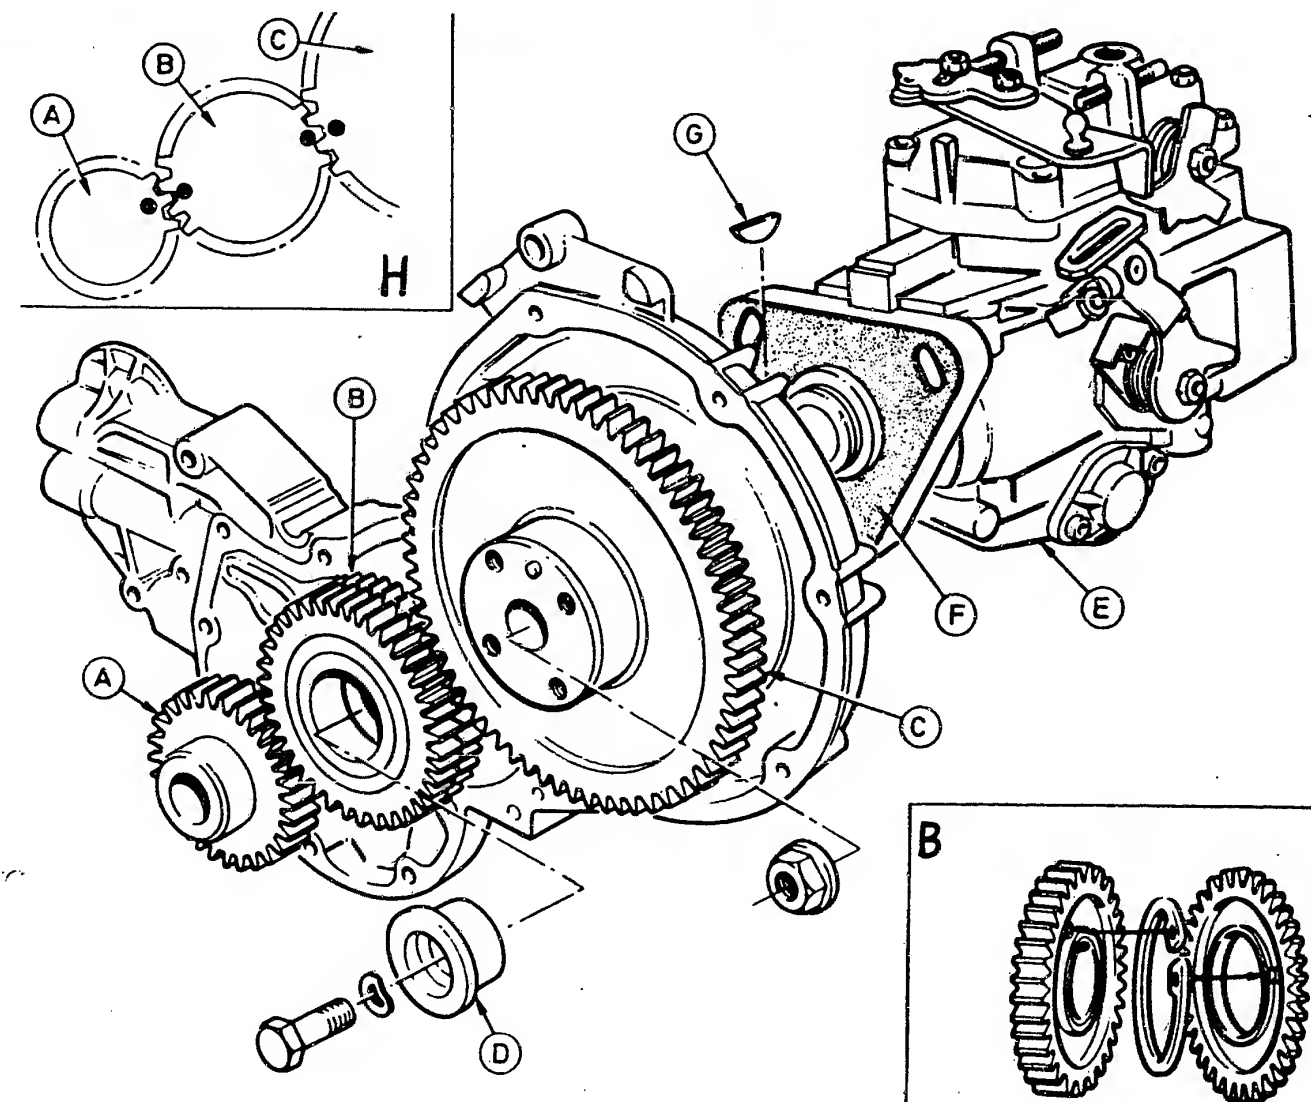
Zusammenbau des Einspritzpumpen-Antriebs: A Kurbelwellen-Zahnrad – B Zwischenrad – C Einspritzpumpen-Zahnrad – D Lagerbüchse – E Diesel-Einspritzpumpe – F Dichtung – G Keil H Zahnradstellung im OT des 1. Zylinders.
